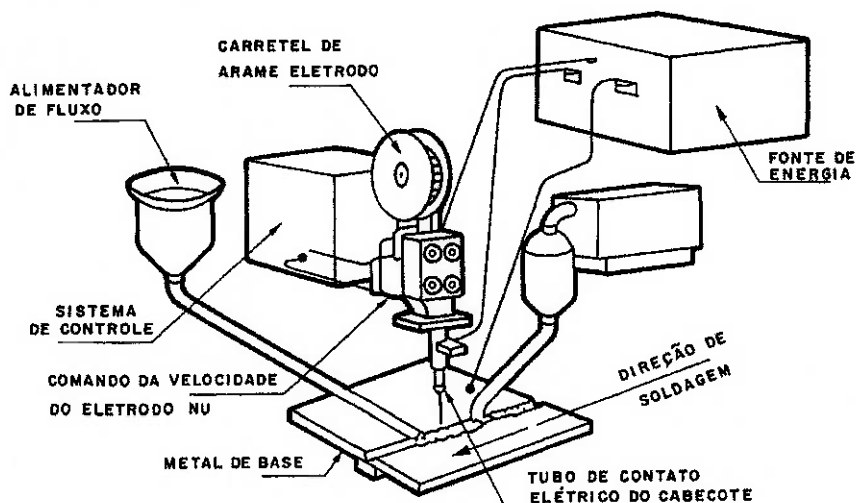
4 – Esquema básico do processo de soldagem Arco Submerso. [2]
